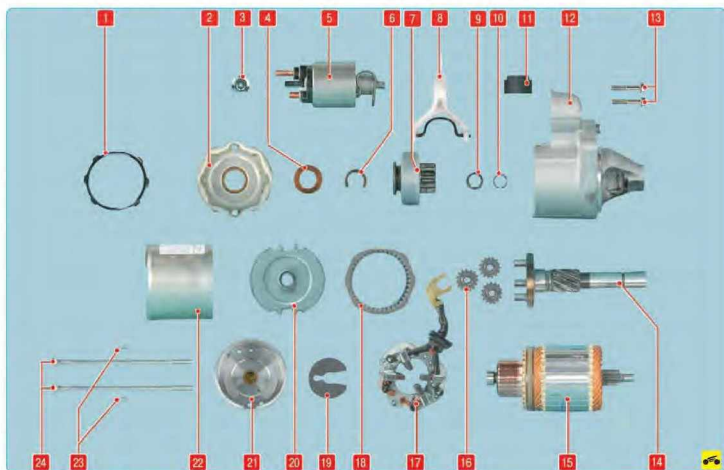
Детали стартера: 1 – уплотнительное кольцо планетарного редуктора; 2 – крышка планетарного редуктора; 3 – гайка контактного болта тягового реле; 4 – дистанционное кольцо привода; 5 – тяговое реле; 6 – стопорное кольцо привода; 7 – муфта привода; 8 – рычаг привода; 9 – упорное кольцо муфты привода; 10 – стопорное кольцо муфты привода; 11 – опора рычага привода; 12 – крышка со стороны привода; 13 – болты крепления тягового реле к крышке со стороны привода; 14 – вал привода; 15 – ротор; 16 – спутник; 17 – щеточный узел; 18 – коронная шестерня; 19 – стопорное кольцо крепления щеточного узла; 20 – маслоотражатель; 21 – крышка со стороны коллектора; 22 – статор; 23 – винты крепления крышки со стороны коллектора; 24 – стяжные болты
